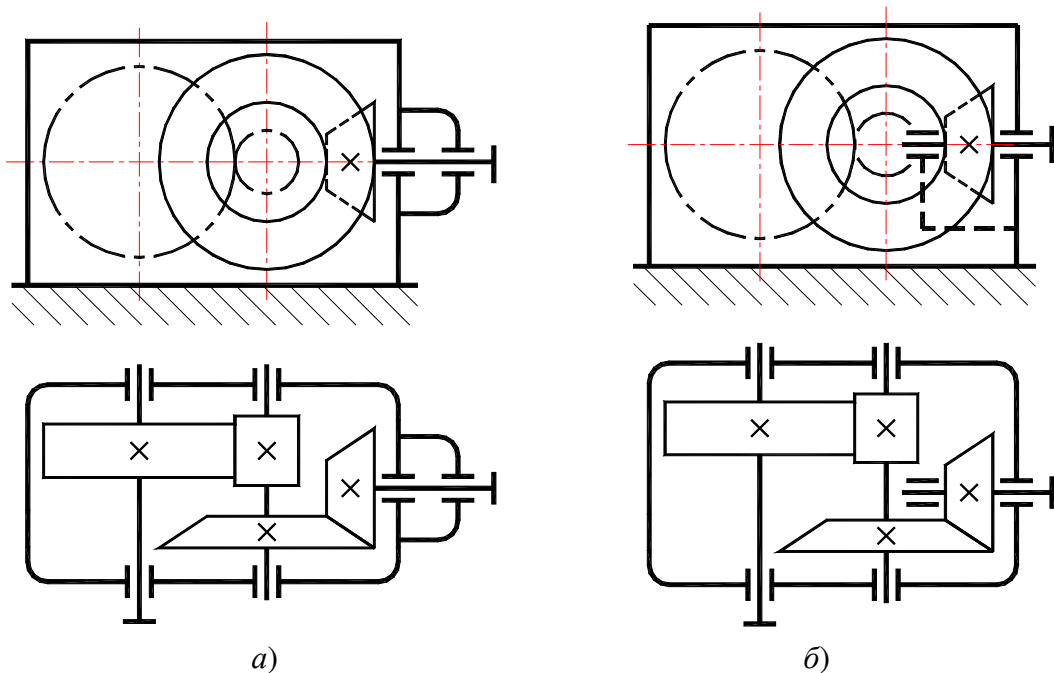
Кинематические схемы коническо-цилиндрических редукторов:
